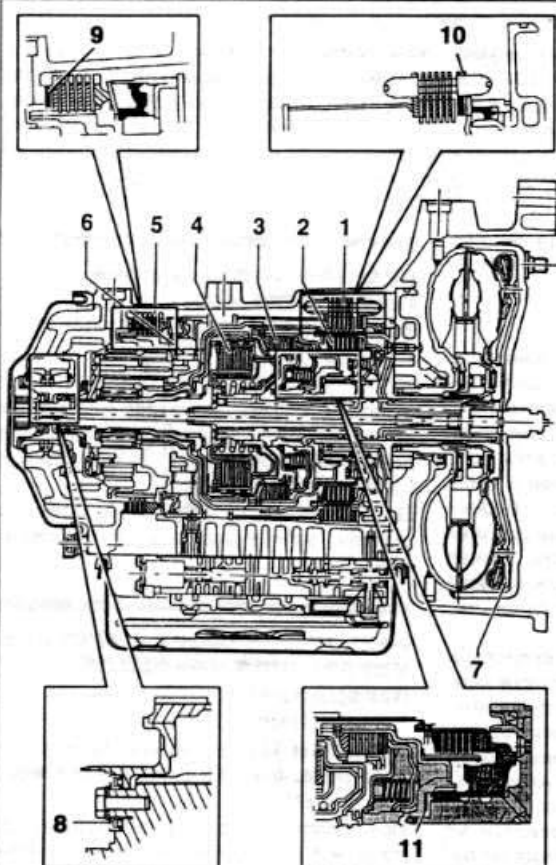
Разрез гидромеханической КП типа 01М и места установки регулировочных колец:
